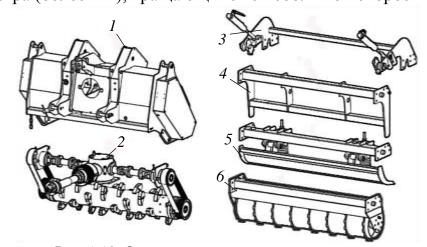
Основные элементы ротоватора: I – корпус фрезы; 2 – ротор с компонентами привода; 3 – адаптер для дополнительного оборудования; 4 – толкающая рама; 5 – грейдерное лезвие; 6 – уплотняющий ролик
